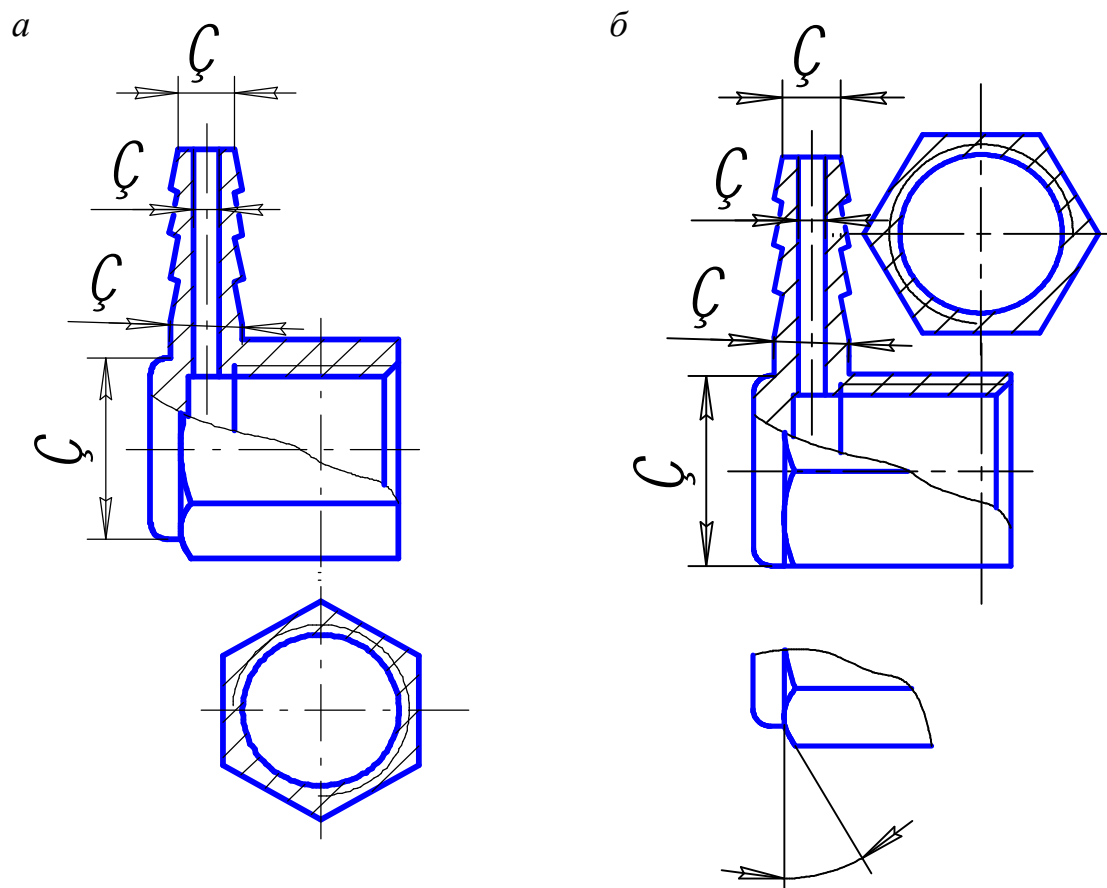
Чертеж накидной гайки со штуцером (а). Увеличение количества изображений на чертеже, произошедшее из-за изменения конструкции детали (б)
